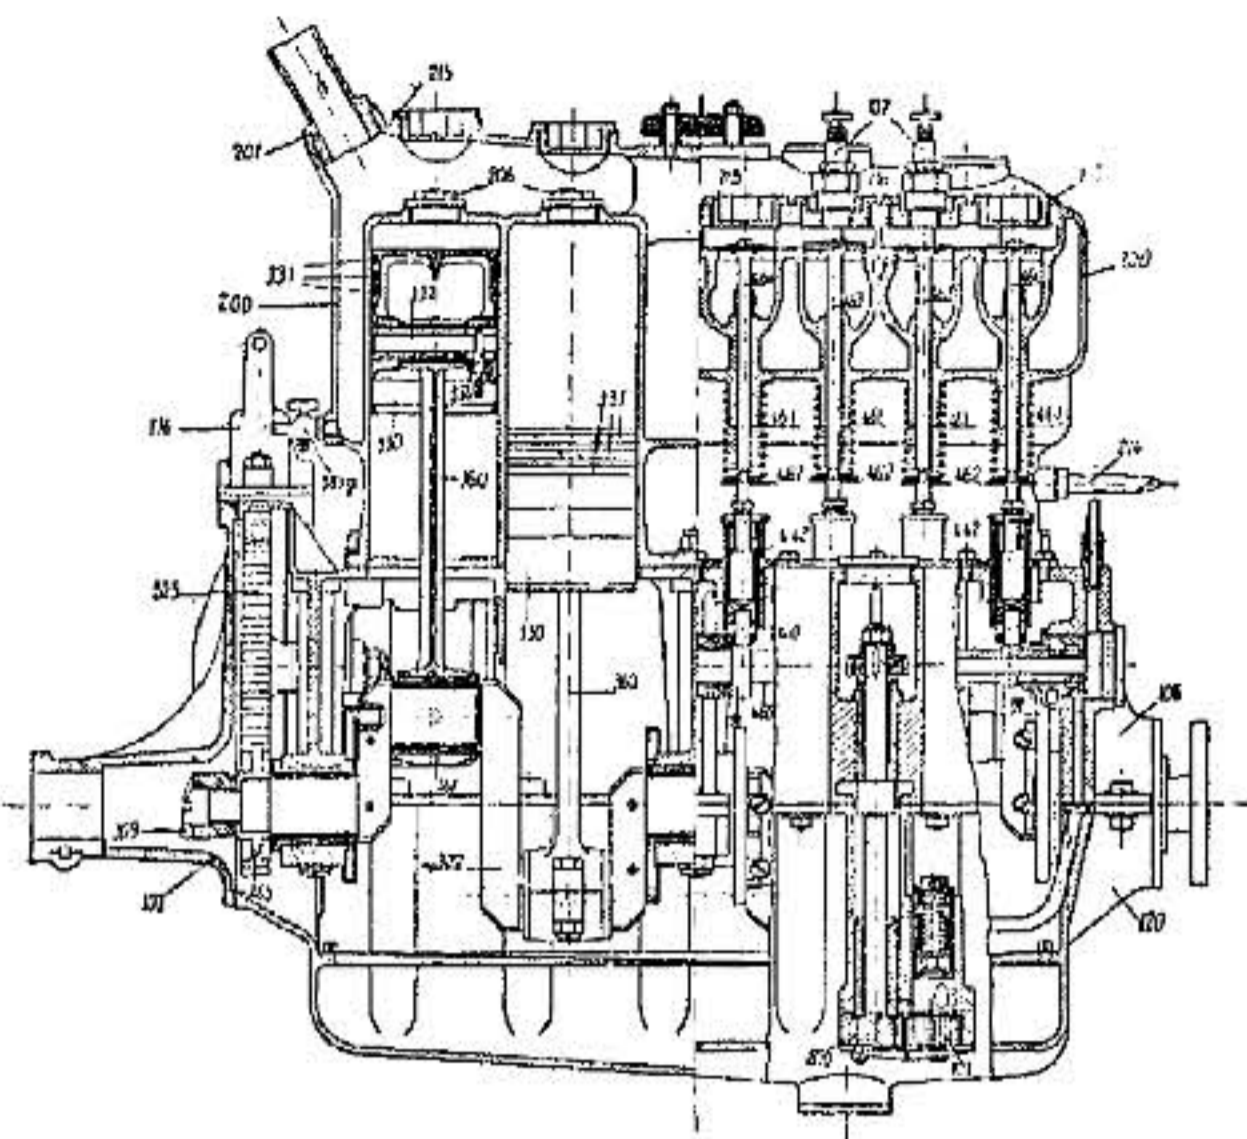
Продольный разрѣзъ двигателя Протосъ.
